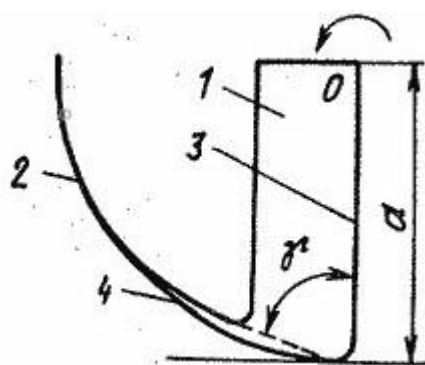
Нож предлагаемой конструкции: 1 – стойка; 2 – крыло; 3, 4 – режущая кромка
